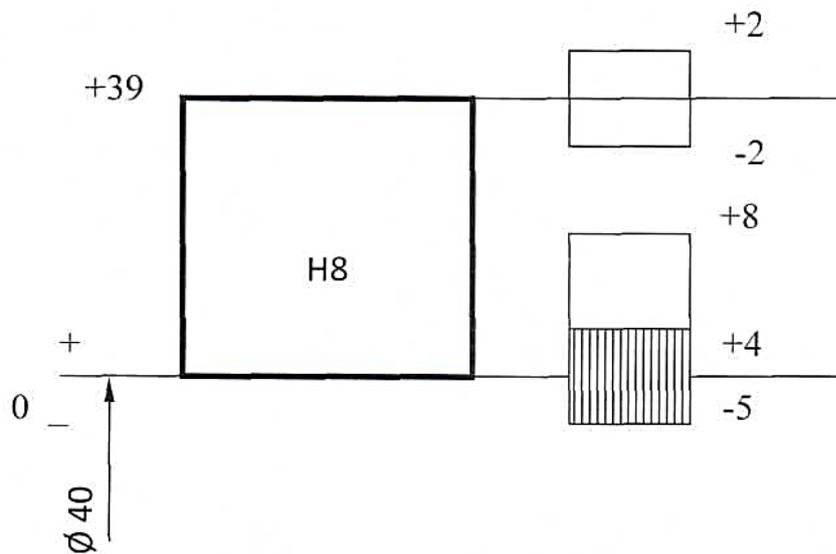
Схема полей допусков калибра-пробки для контроля отверстия $\varnothing 40$ H8
